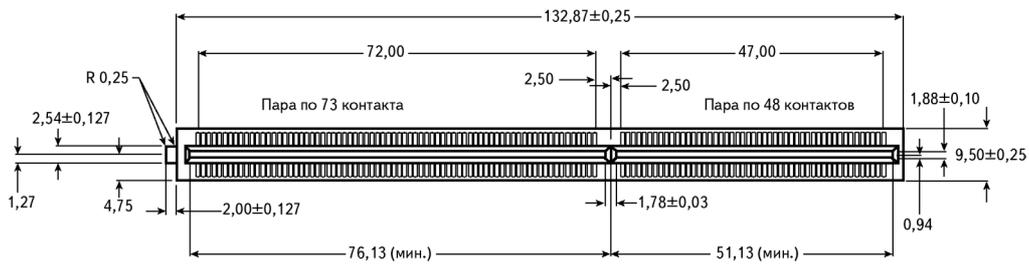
Размеры разъема Slot 1 для процессора Pentium II
